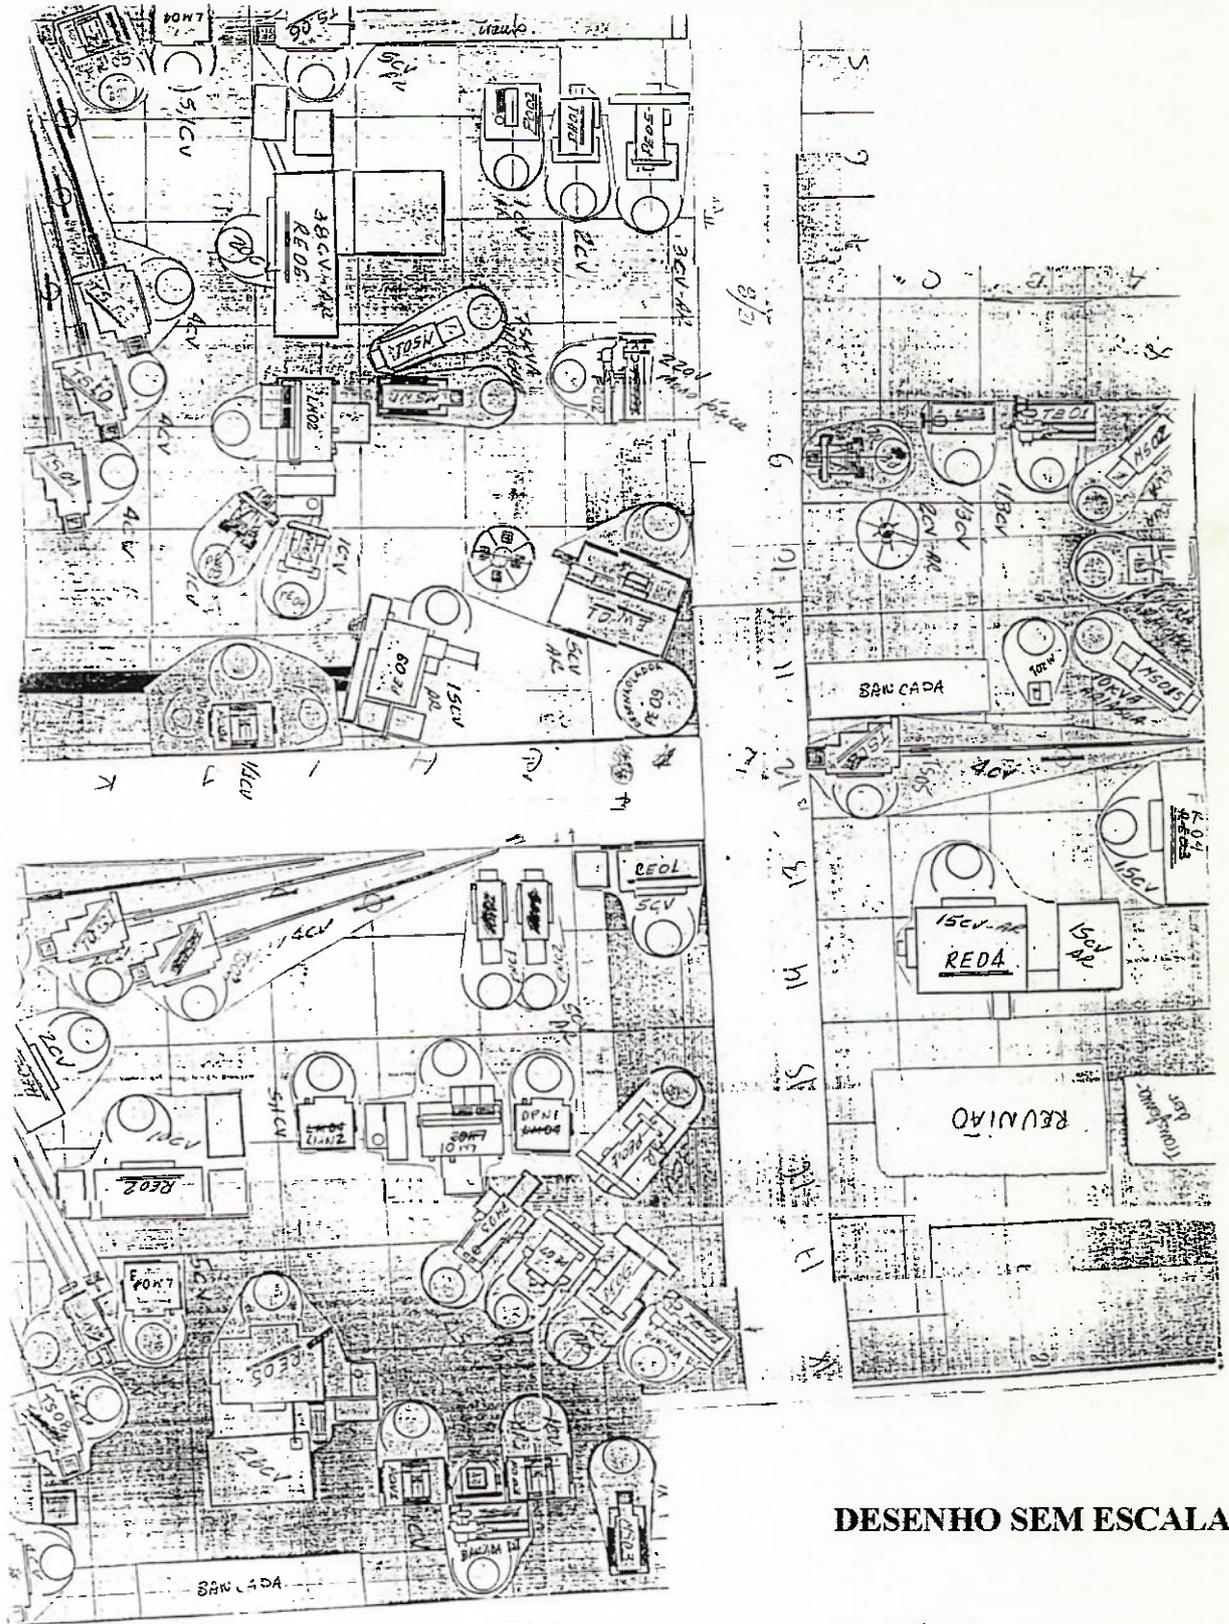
Lay-out detalhado. (Elaborado pelo Autor e Consultor).
